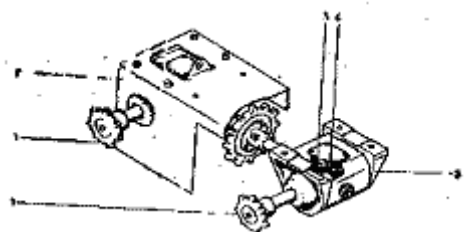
Редукторы с крышкой нижней головки загрузочного транспортера:
